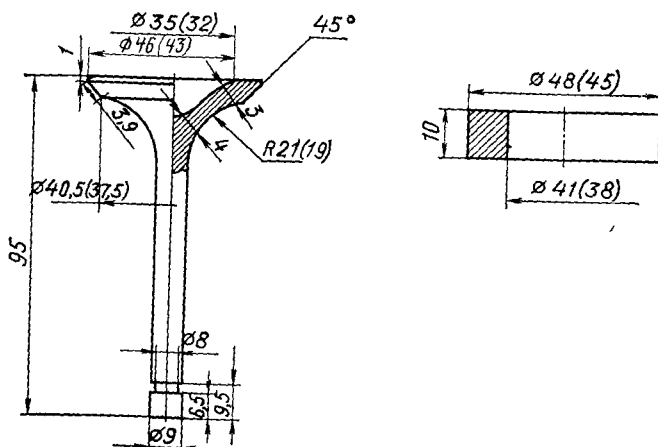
Предельные размеры клапана и седла, устанавливаемых в головке двигателя мотоцикла К-650
